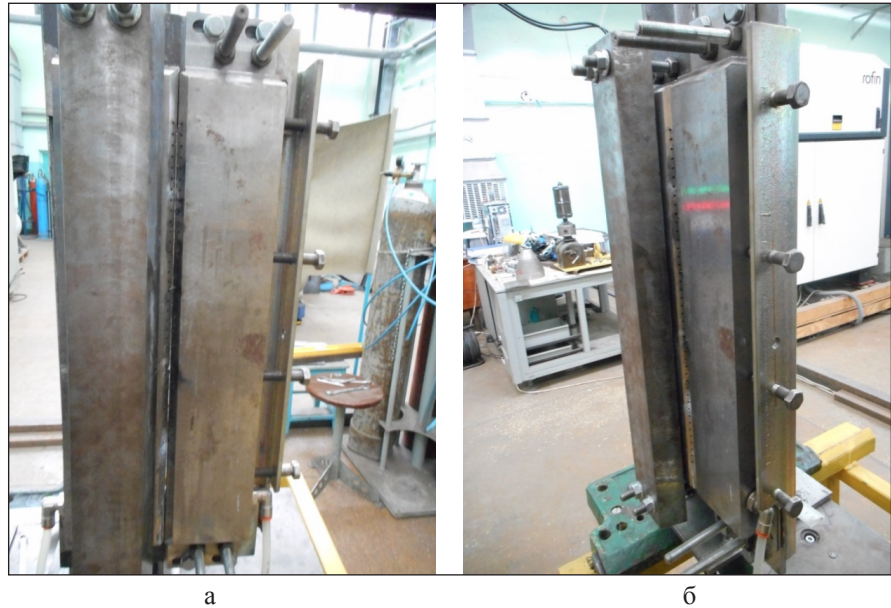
Зовнішній вигляд струбцини для зварювання таврових зварних з'єднань: а – з лицьової сторони; б – збоку
